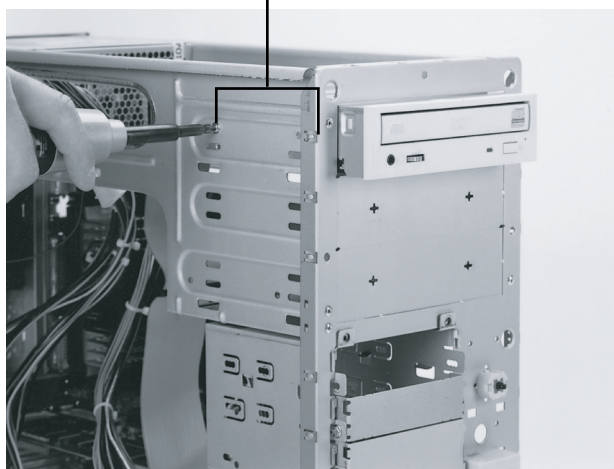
Закрепление накопителя в корпусе с помощью винтов
